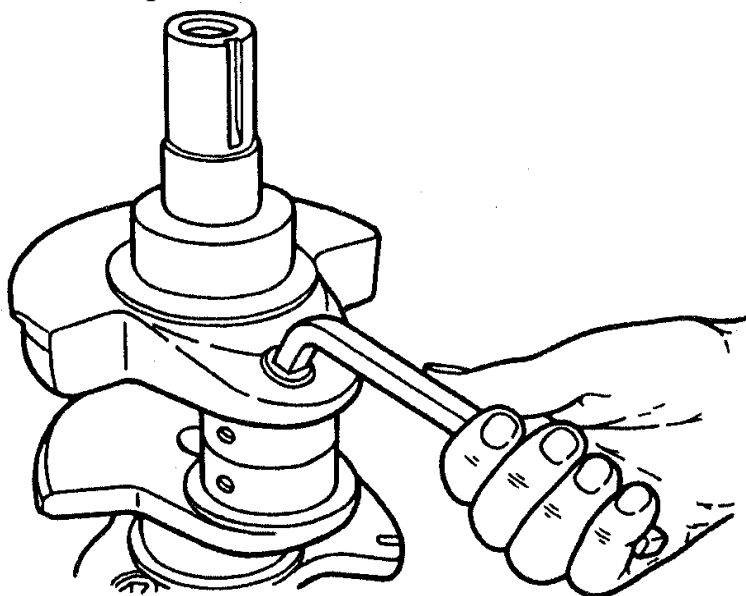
Вывертывание пробок грязеуловителей из коленчатого вала
